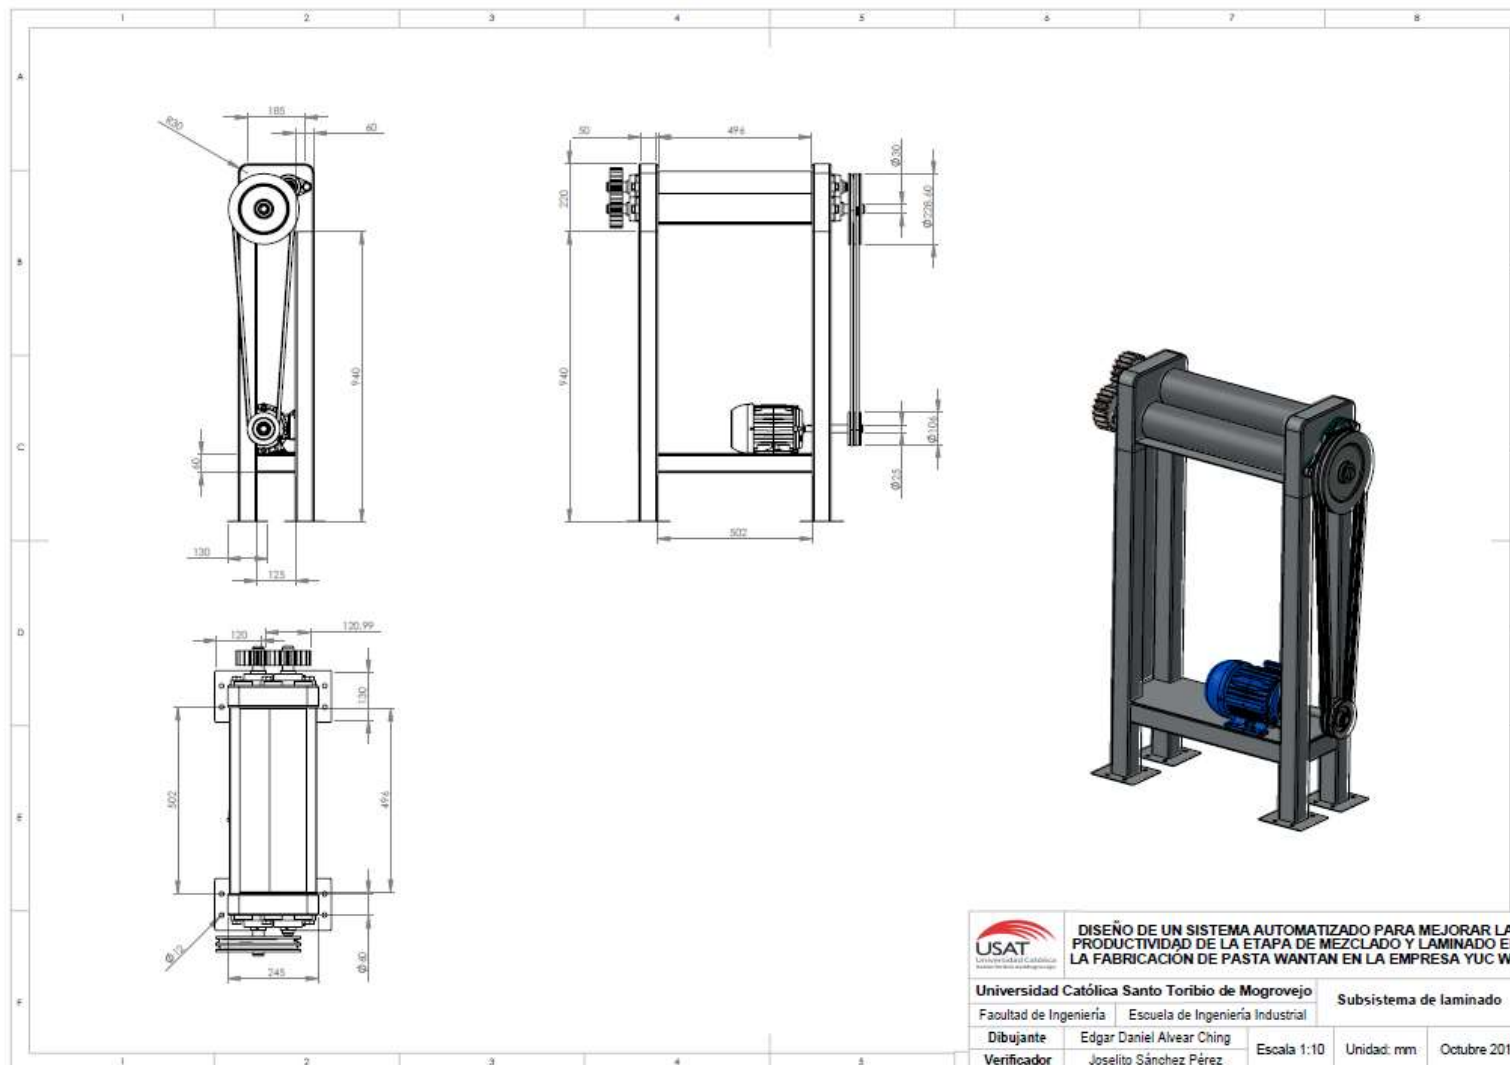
Plano esquemático del subsistema de laminado con sus tres vistas principales
